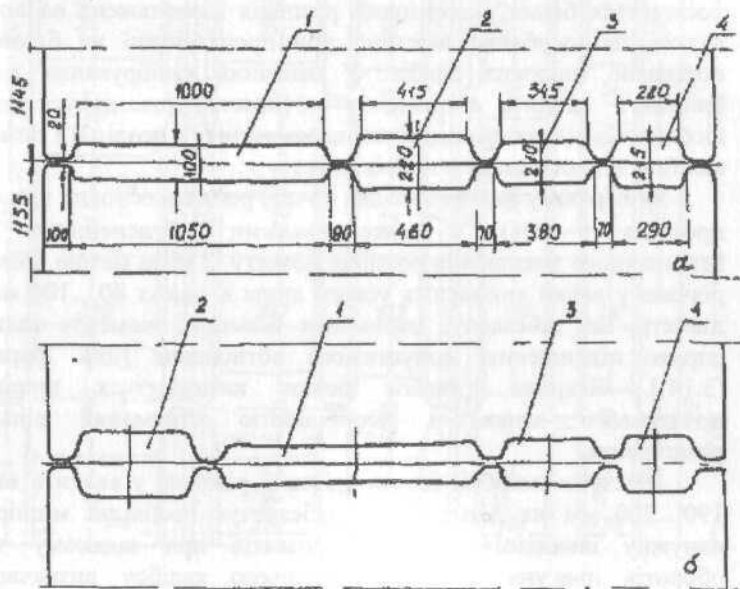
Схеми розташування калібрів : а - з гладкою бочкою з краю валка; б - в середині.
